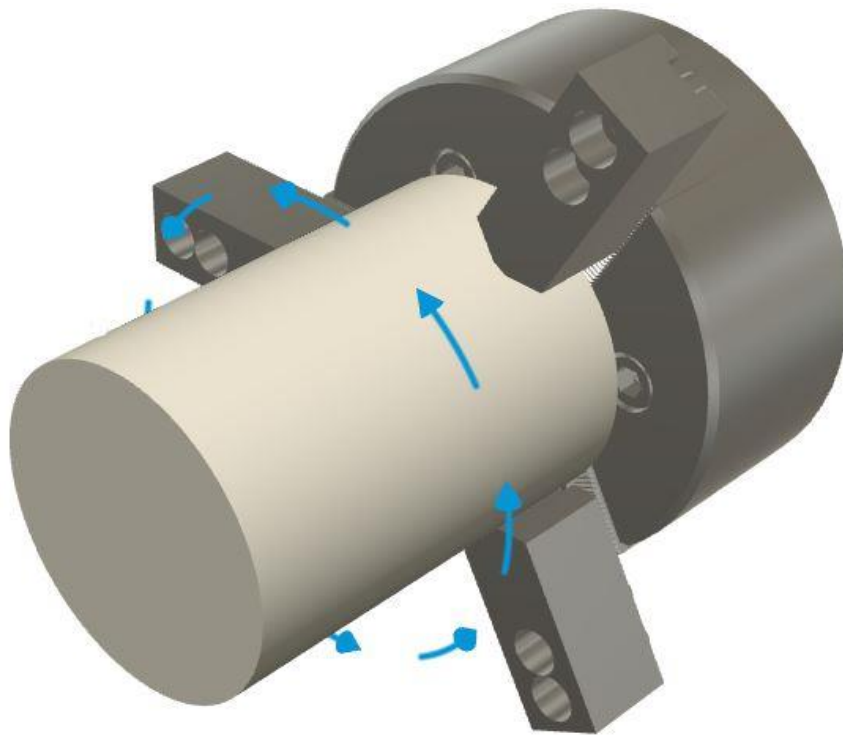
Заготовка встановлена в самоцентрівний трьохкулачковий патрон
